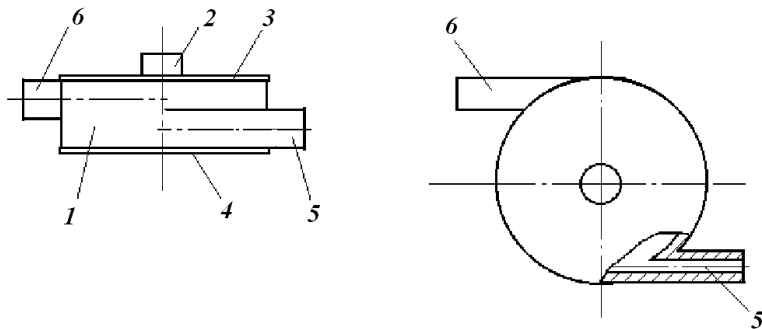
Вихревая мельница: 1 – помольная камера; 2 – загрузочный патрубок; 3, 4 – торцевые крышки; 5 – патрубок подачи сжатого воздуха; 6 – патрубок отвода материала.
